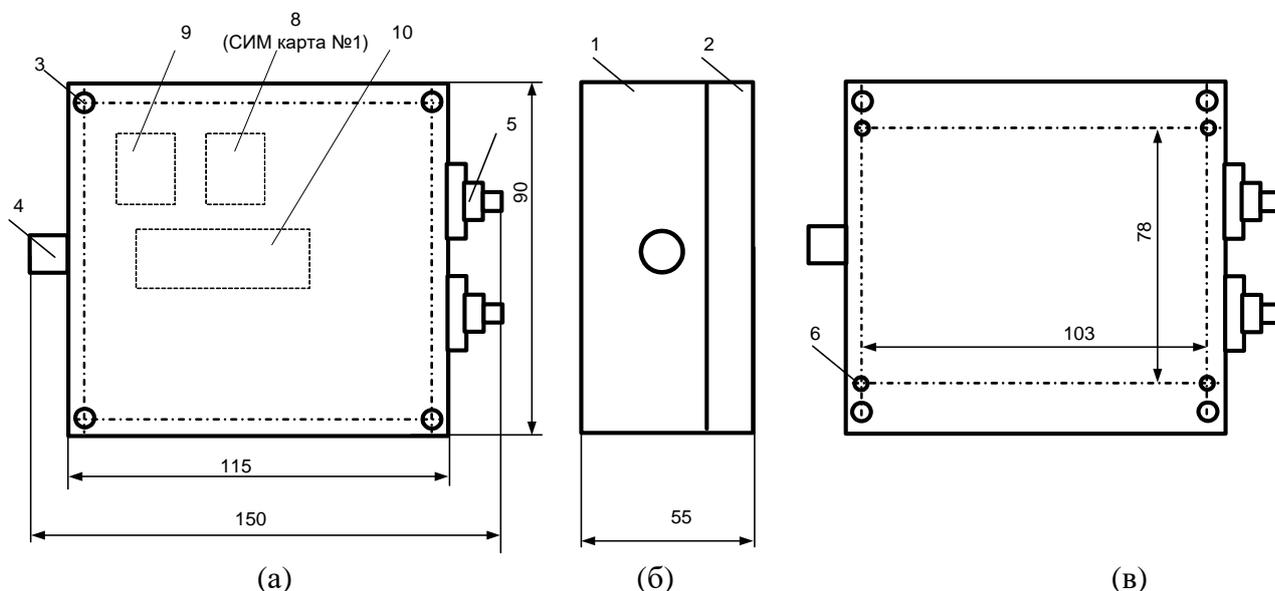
габаритные (а и б) и установочные (в) размеры GSM регистратора
